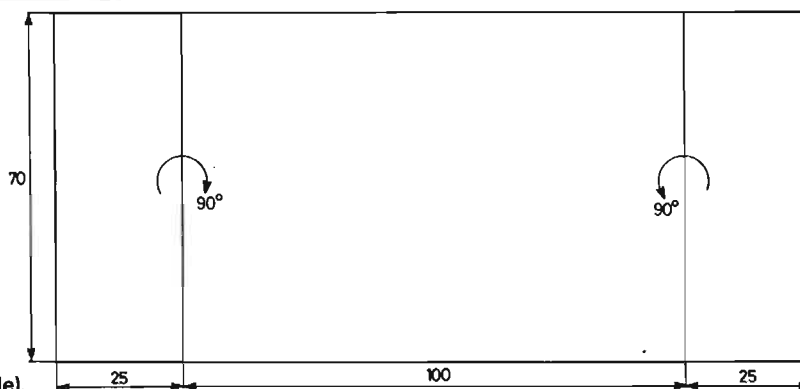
Plan du boîtier (alu de 10/10 par exemple).
